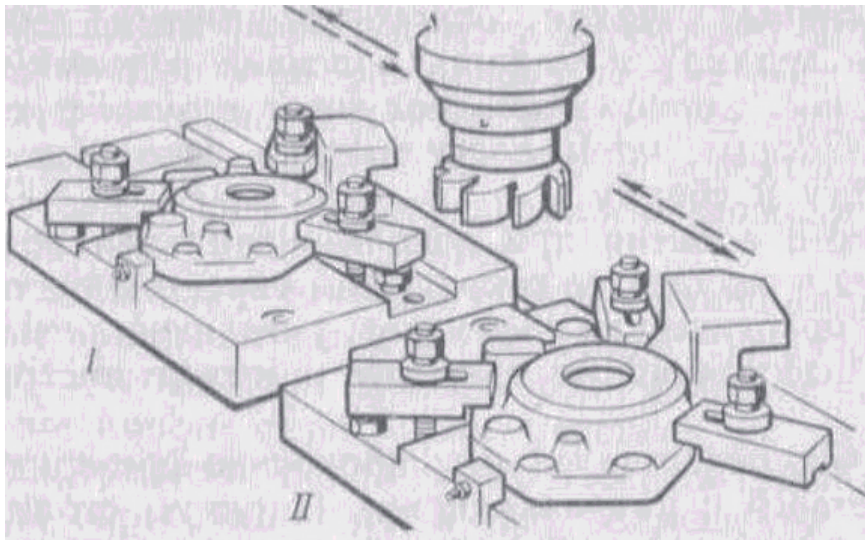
Обработка двух заготовок на универсально-фрезерном станке по «маятниковой» схеме
